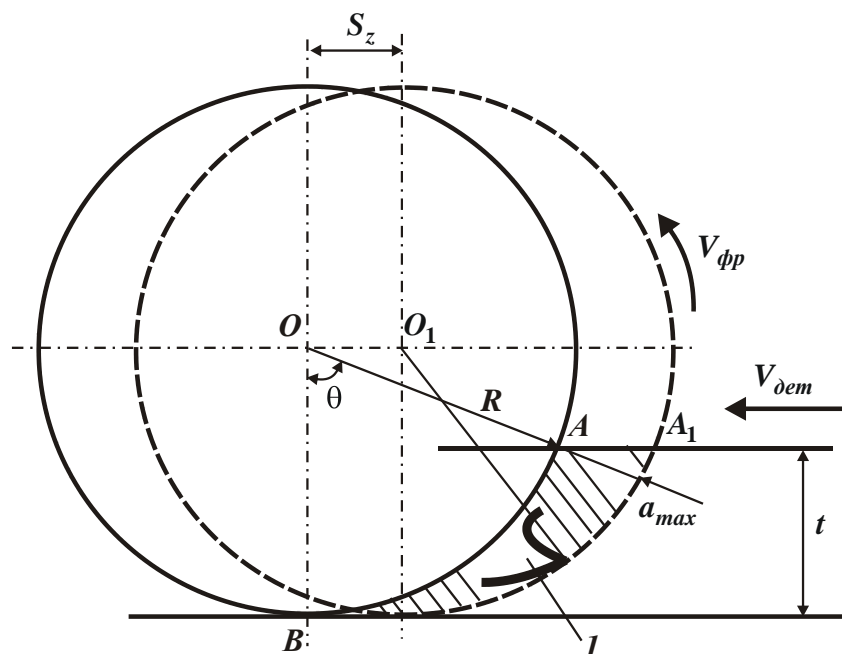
Розрахункова схема параметрів процесу фрезерування циліндричною фрезою: 1 – зуб фрези
